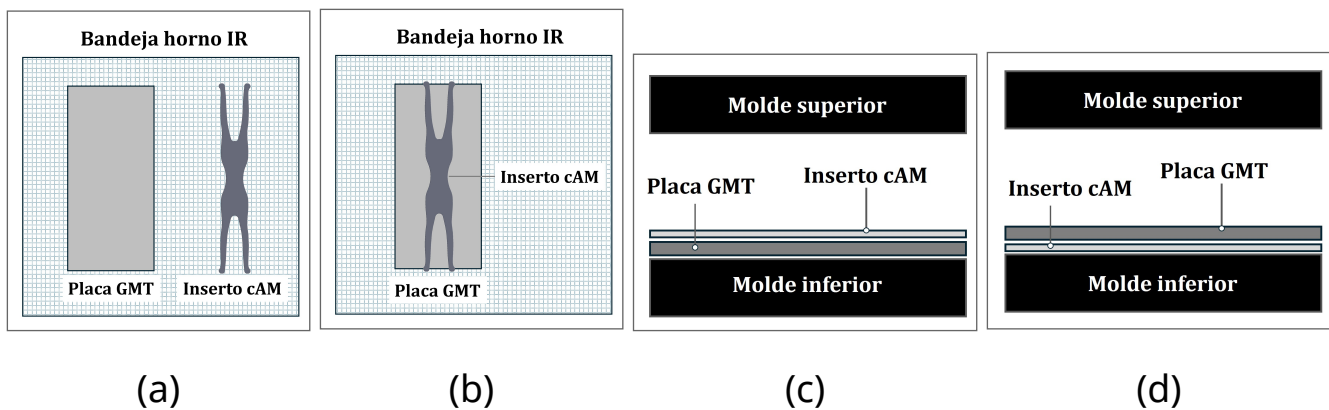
Proceso calentamiento con inserto cAM separado del GMT (a), y encima de GMT (b). Posición en el molde del inserto cAM encima de GMT (c), y debajo de GMT (d).
